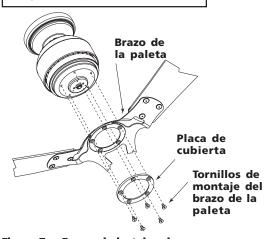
Forma de instalar el soporte de metal con las paletas en el motor
